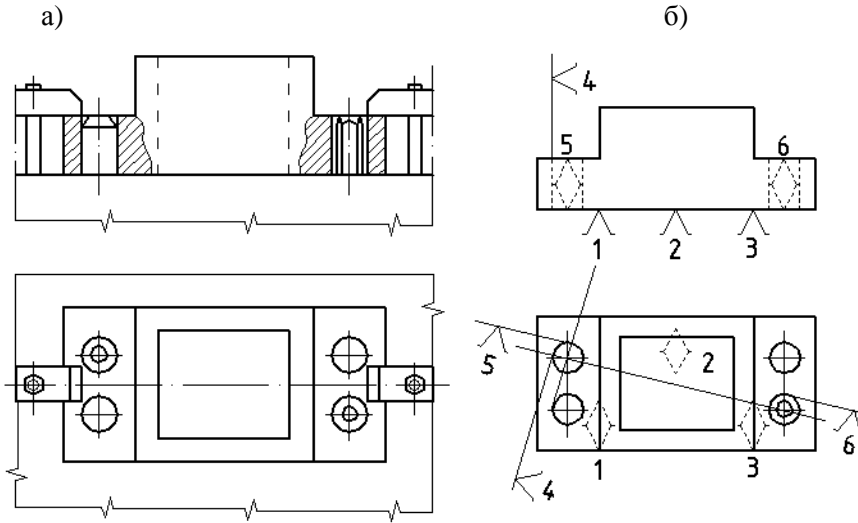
Установка заготовки в приспособление (а) и теоретическая схема базирования (б)
